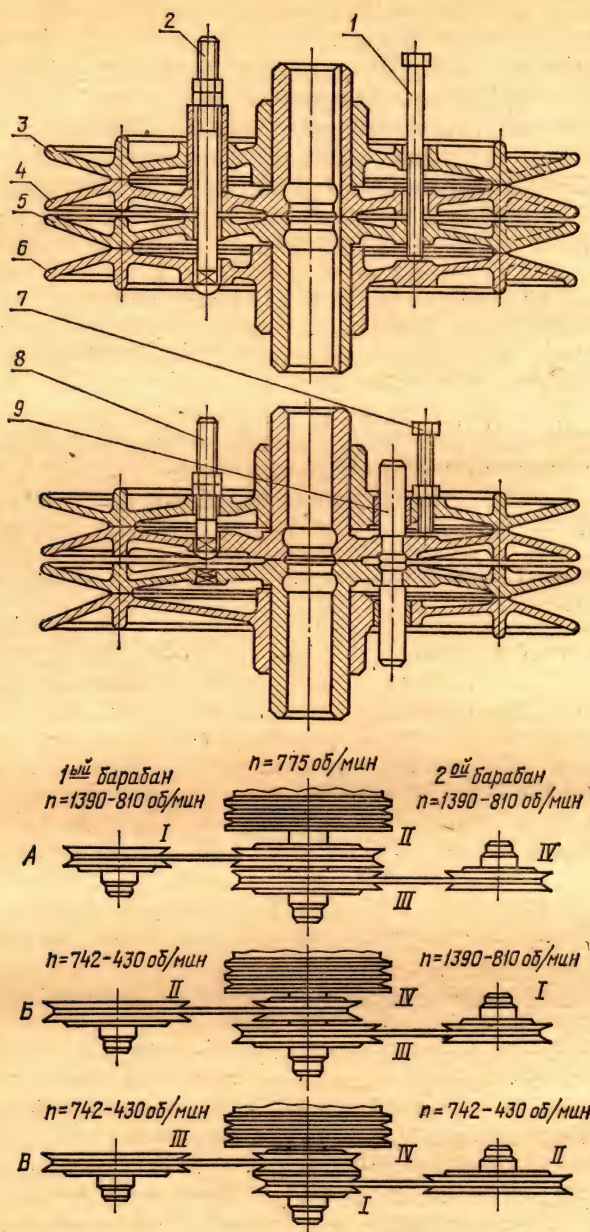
Блок вариатора и схемы перестановки шкивов главного контрприводного вала и барабанов комбайна СКД-5:
